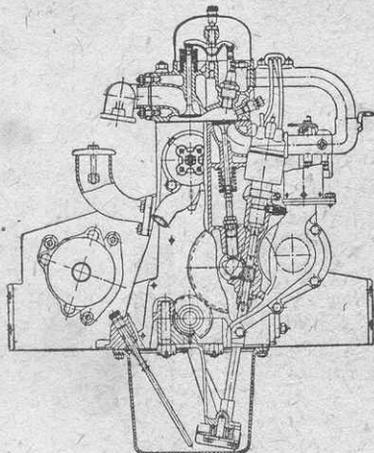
Поперечный разрез двигателя «Бреннабор» 6/25 л. с.
